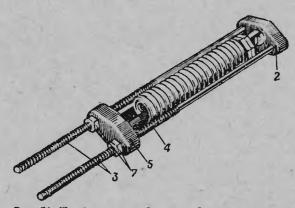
Прибор для разборки и сборки компенсирующего механизма: 2— передиий фланец: 3— штанги: 4— чека; 5— задний фланец; 7— гайкн
